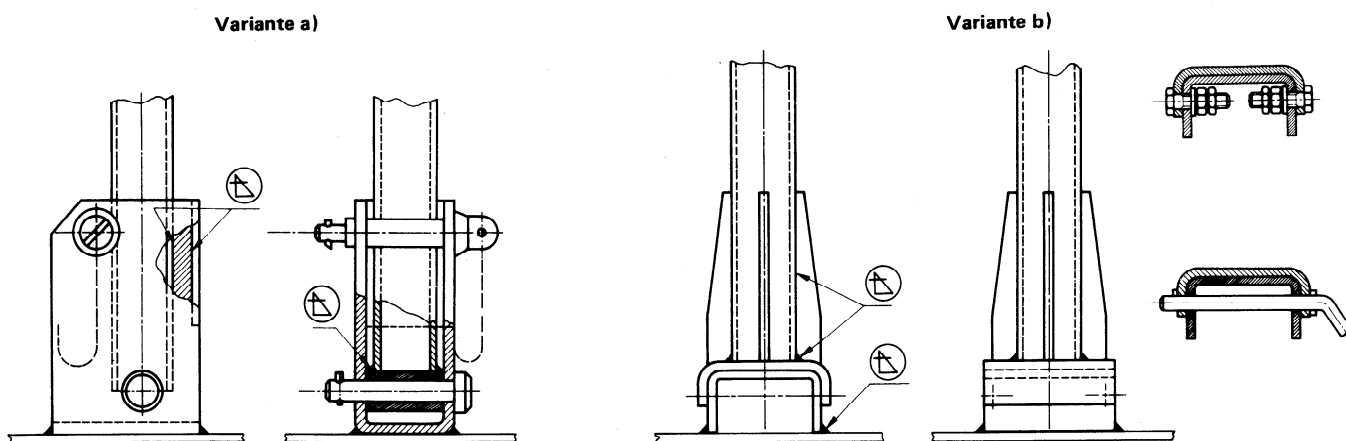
Installation des chandeliers du garde-corps rabattable
